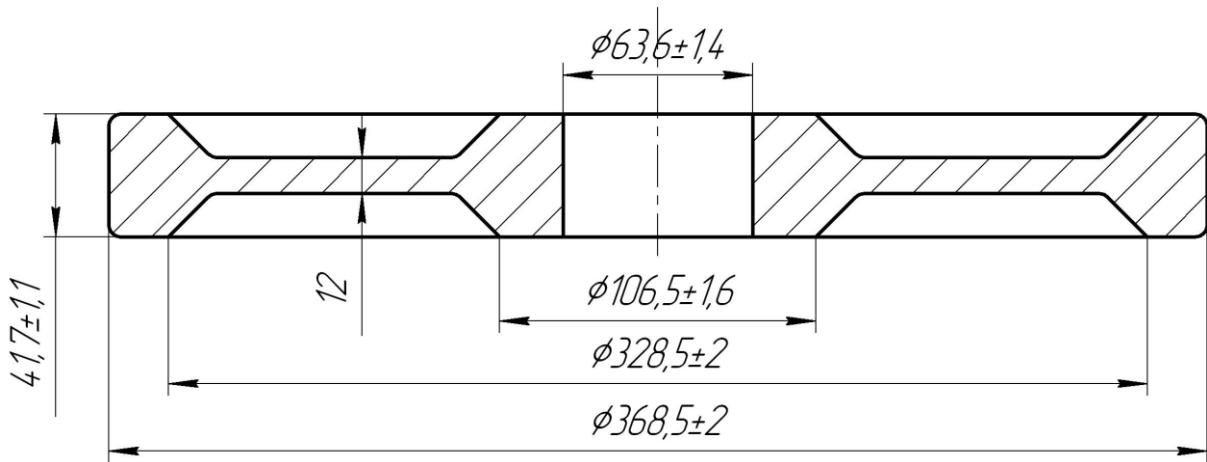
Эскиз отливки (эскиз детали см. рис. 3).
